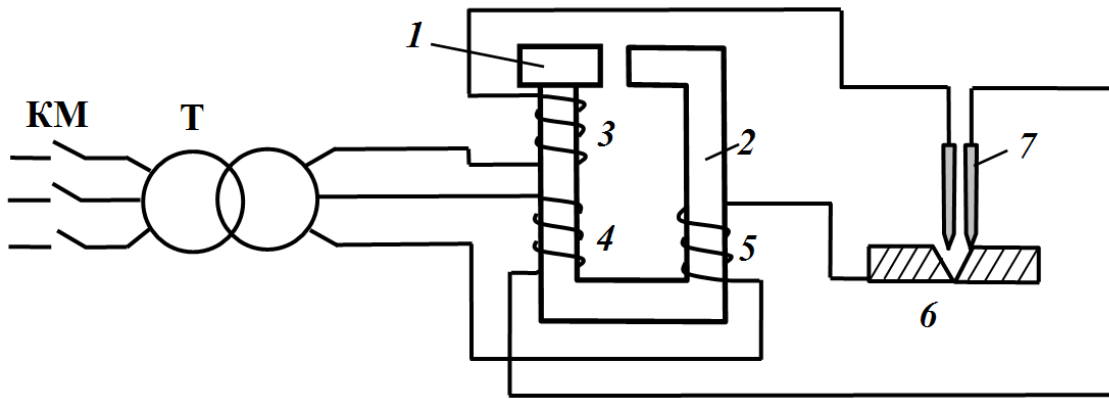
Трифазний зварювальний трансформатор:
